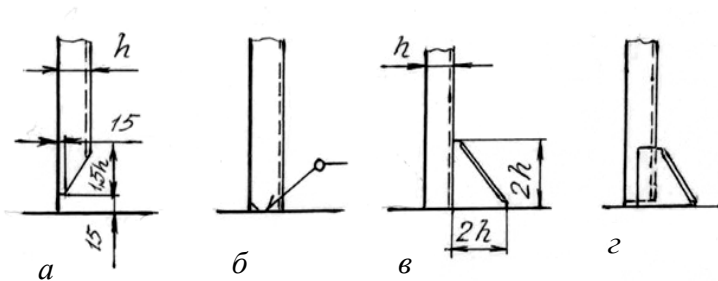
Схемы крепления концов балок набора переборок:
